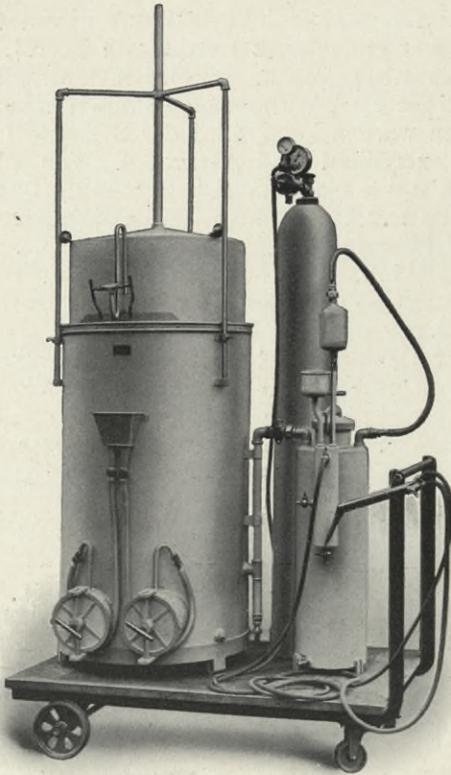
Acetylen-Sauerstoff-Schweißanlage
